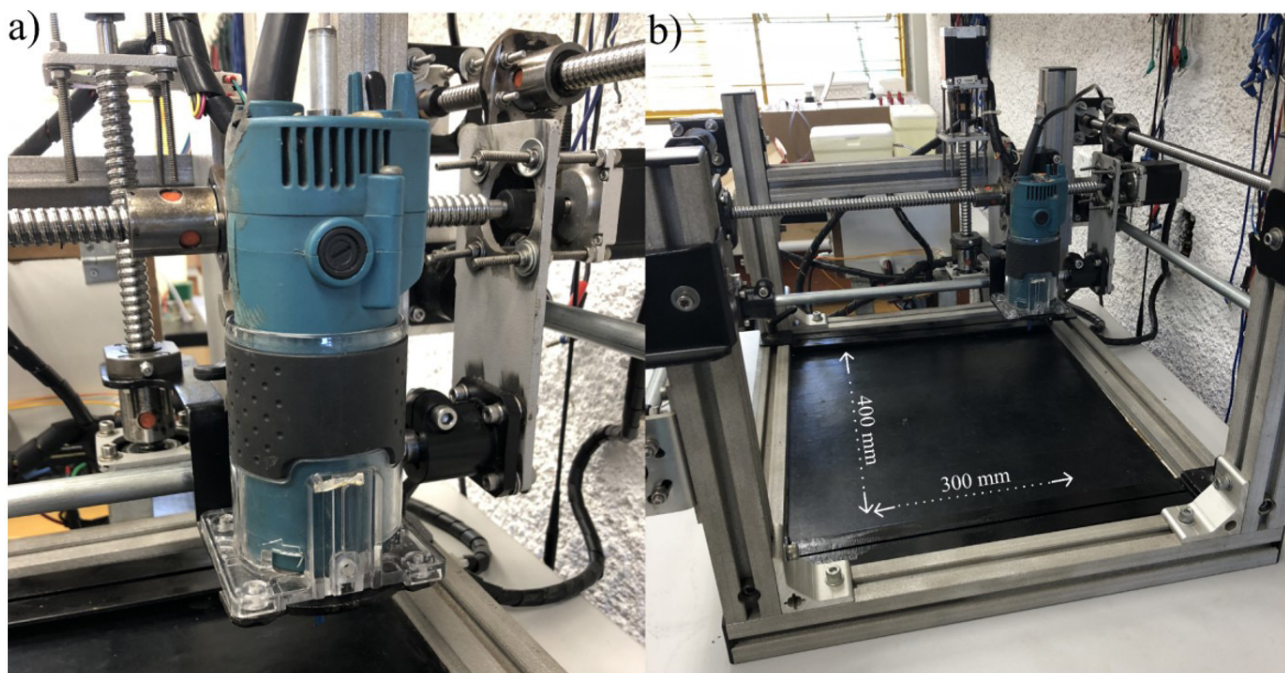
(a) Tupa fixada na máquina. (b) Área de trabalho para fresagem CNC. Adaptado de Delmondes e Rodrigues [47].
